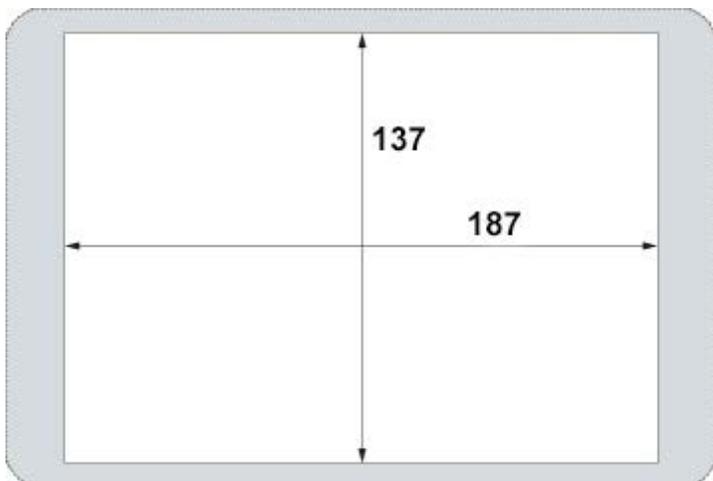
Découpe de montage GUI607 (dimensions en mm)
